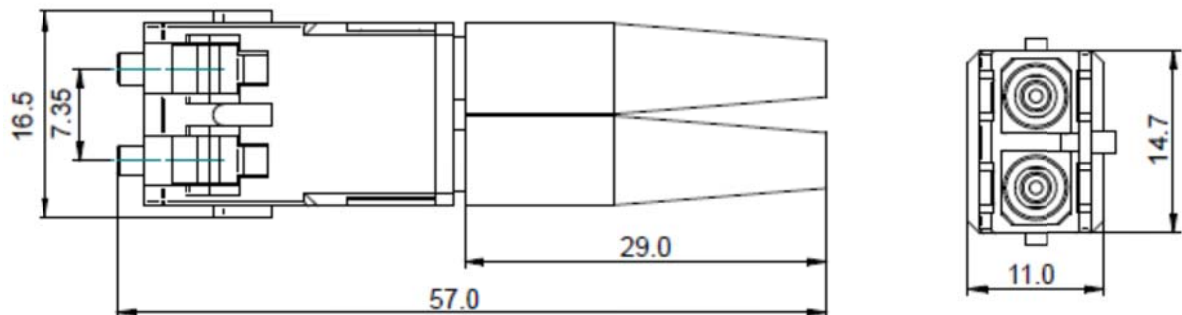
SC-RJ Steckverbinder/Connector
